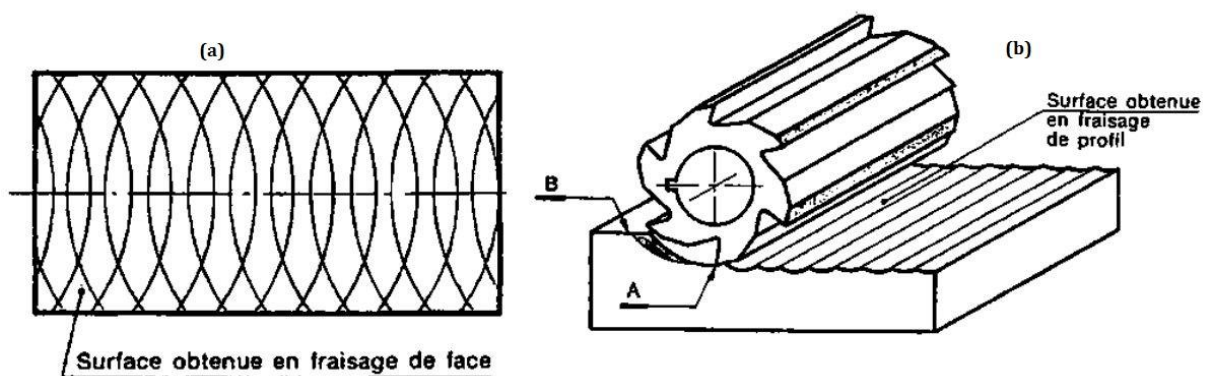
Forme de surfaces obtenues par le fraisage en bout (a) et le fraisage en roulant (b) [6]
